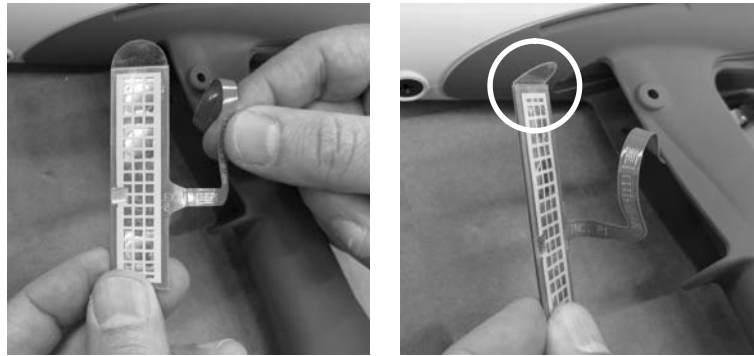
Installazione dell'interruttore del grilletto – Punto 3
